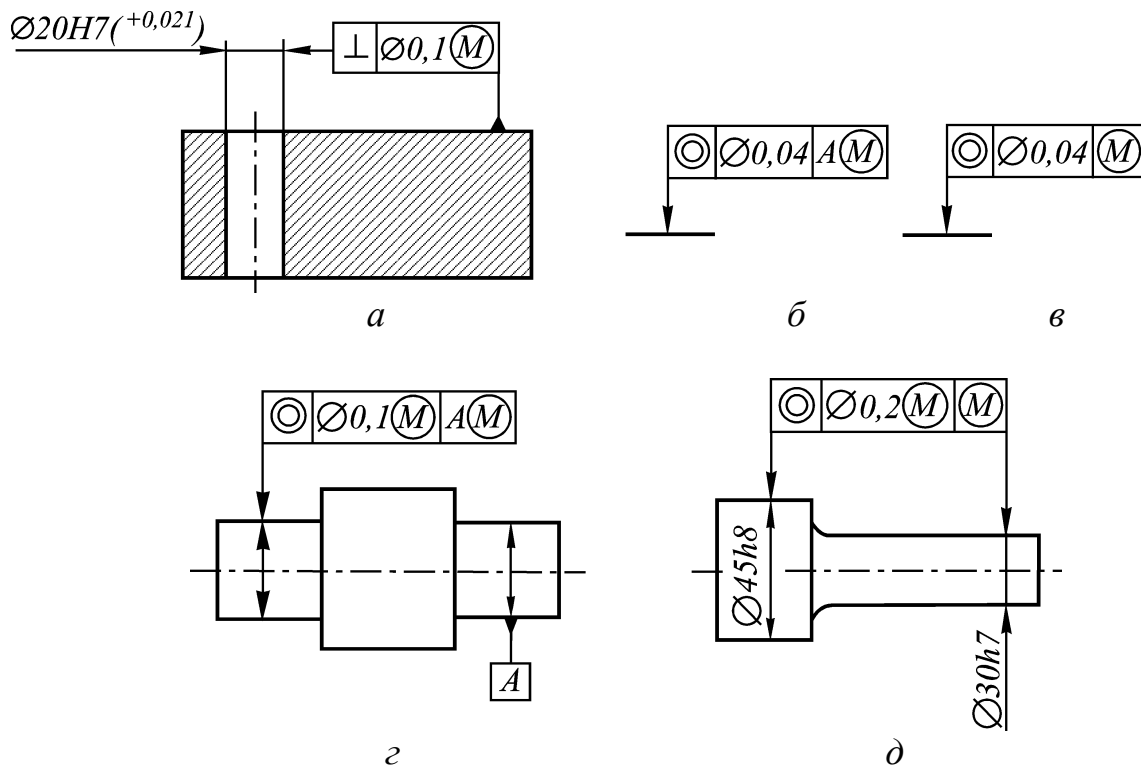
Обозначение на чертежах зависимых допусков формы и расположения поверхностей
